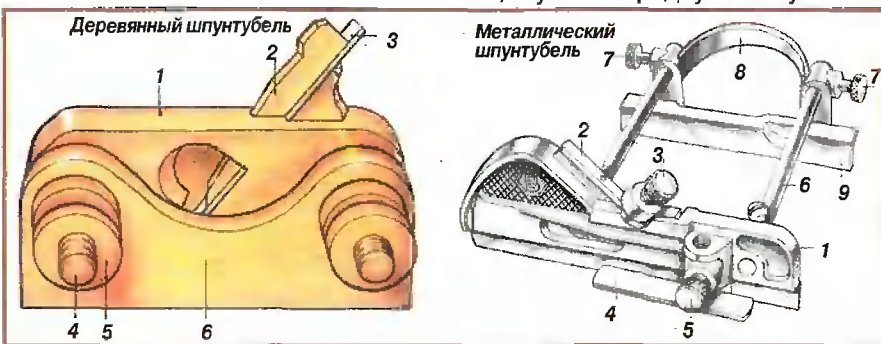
Деревянный шпунтубель: 1 — основная колодка; 2 — клин; 3 — нож; 4 — винт; 5 — гайка; 6 — дополнительная колодка (упорная планка). Металлический шпунтубель: 1 — корпус; 2 — нож; 3 — винт крепления ножа; 4 — упор; 5 — винт крепления упора; 6 — штифт; 7 — винты рукоятки; 8 — рукоятка; 9 — упорная планка.
